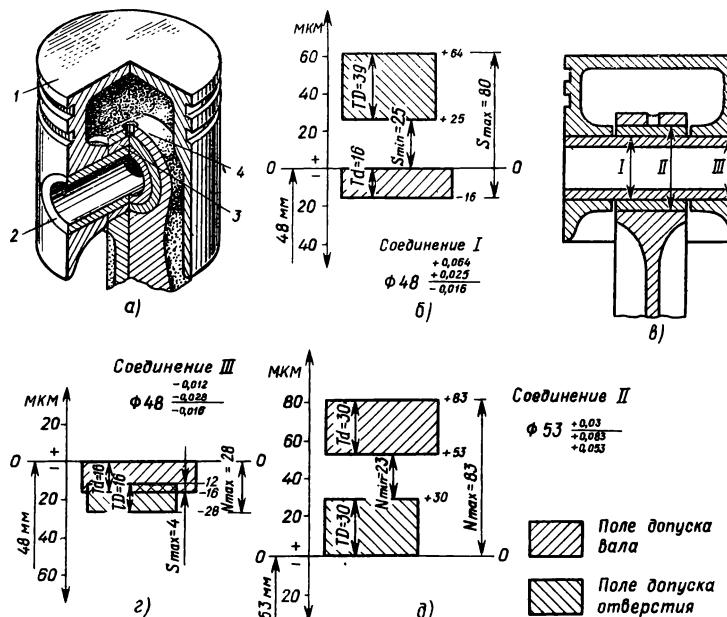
Детали поршневой группы в сборе (а) и их сборочный чертеж (б), обозначения на чертеже соединения деталей и схема расположения полей допусков для посадки с зазором (б), переходной посадки (в) и посадки с натягом (д): 1 – поршень; 2 – поршневой палец; 3 – втулка верхней головки шатуна; 4 – шатун
